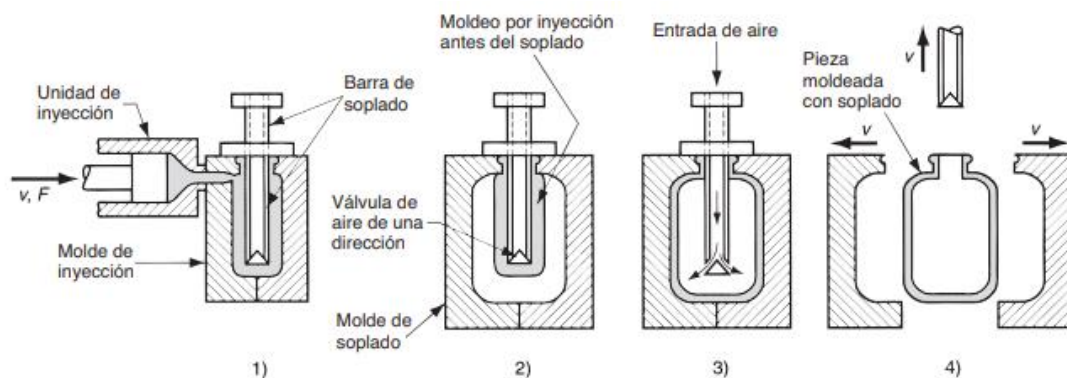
Moldeo por soplado e inyección. Fuente: Groover, M. P. (2007). *Fundamentos de manufactura moderna: materiales, procesos y sistemas* (3ª ed., p. 291). McGraw-Hill.
